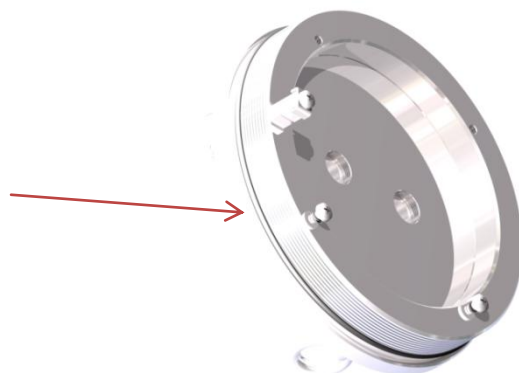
Position der O-Ring-Dichtung Typ T08-TNXCD
